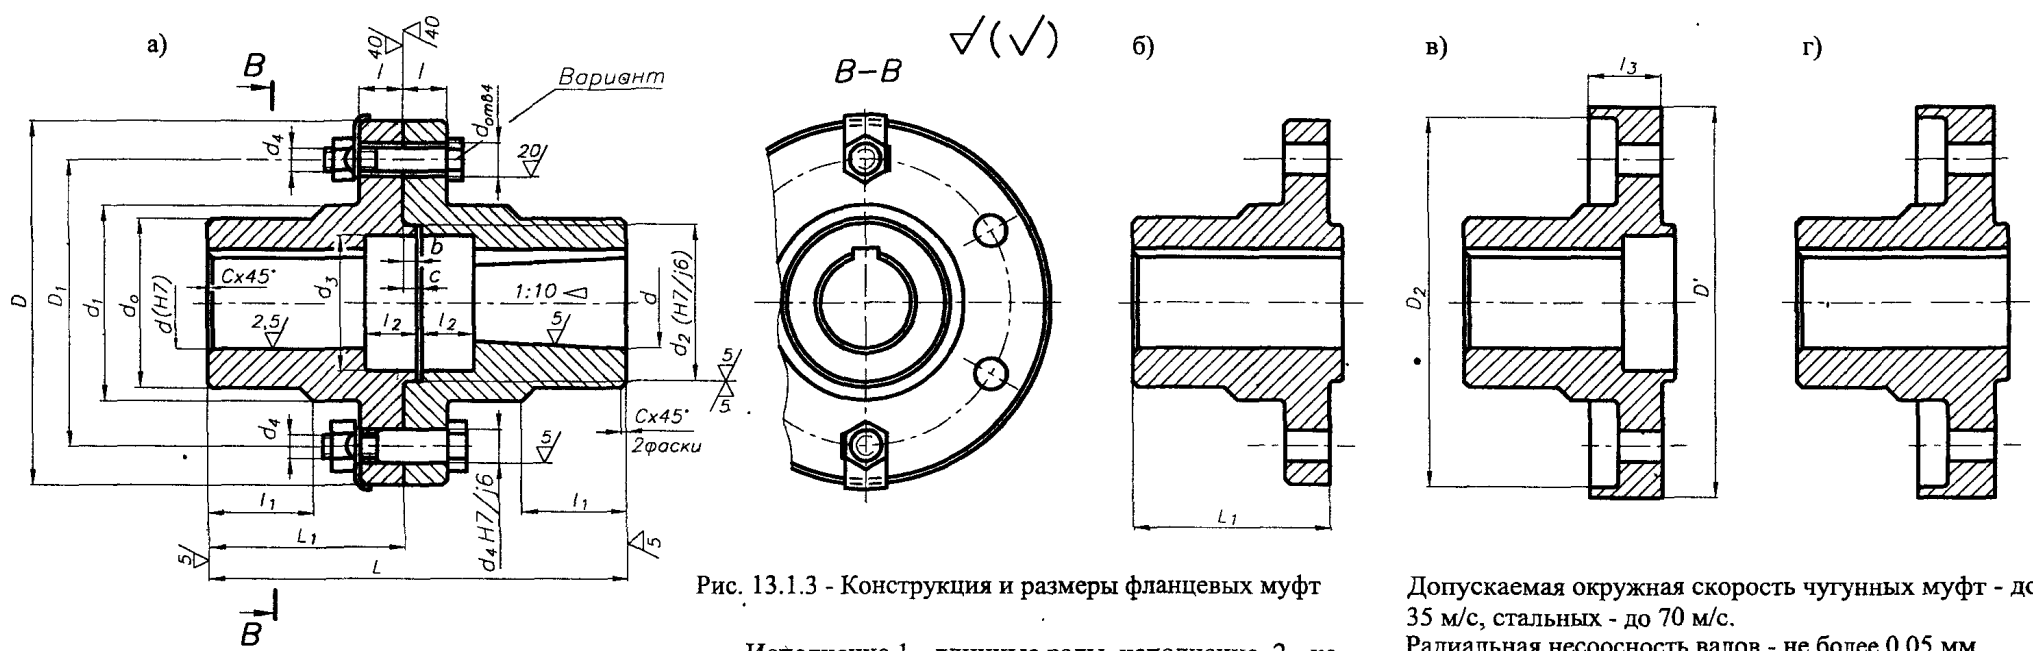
Конструкция и размеры фланцевых муфт
